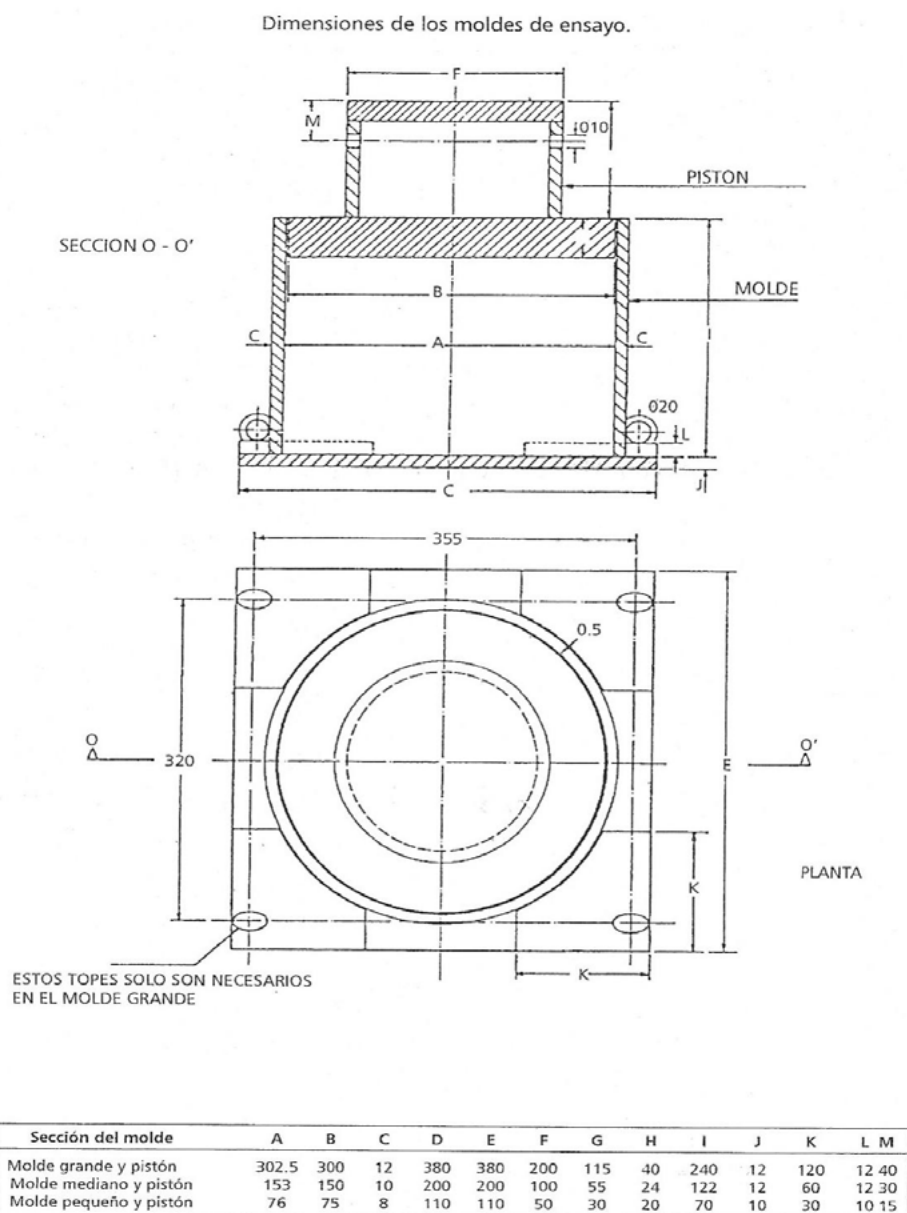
8. DIMENSIONES DE LOS MOLDES DE ENSAYO
